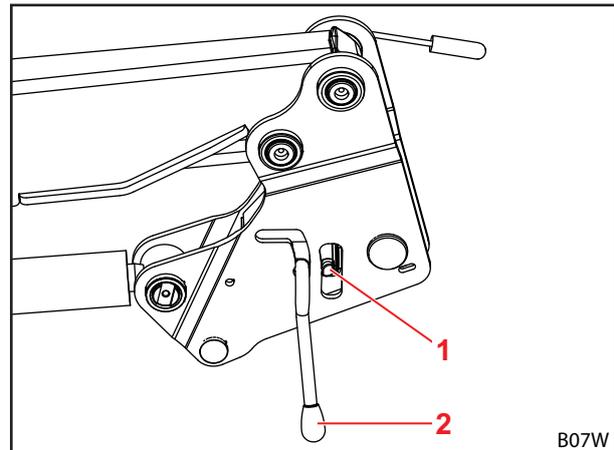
Verificare il dispositivo di bloccaggio del caricatore frontale
